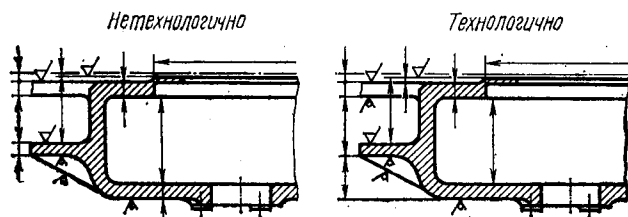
Простановка размеров между обрабатываемыми поверхностями или необрабатываемыми.
